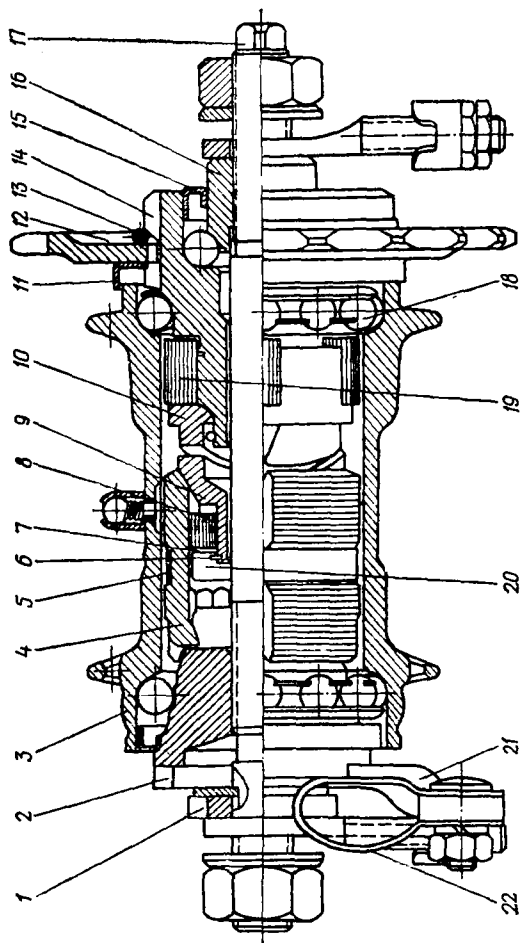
Втулка заднего колеса тормозная со свободным ходом:
